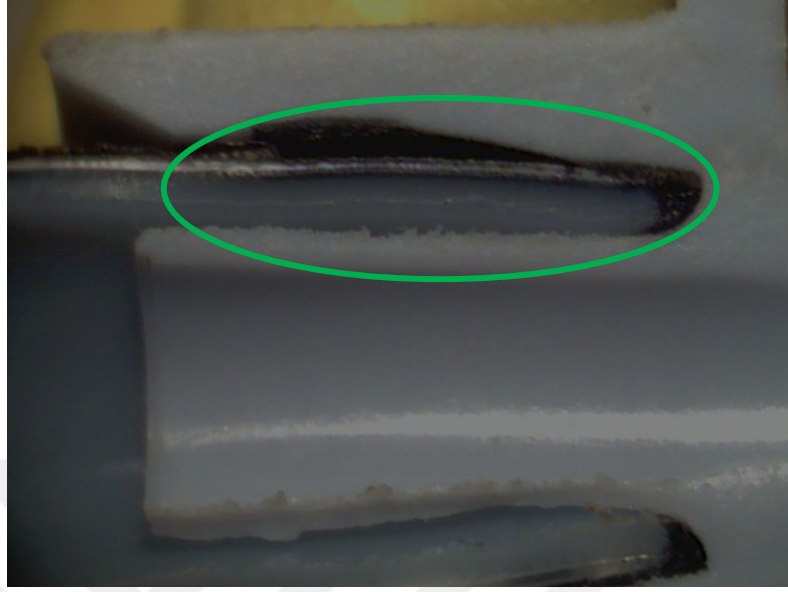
PA12LX9013 Kaynak bölgesi
